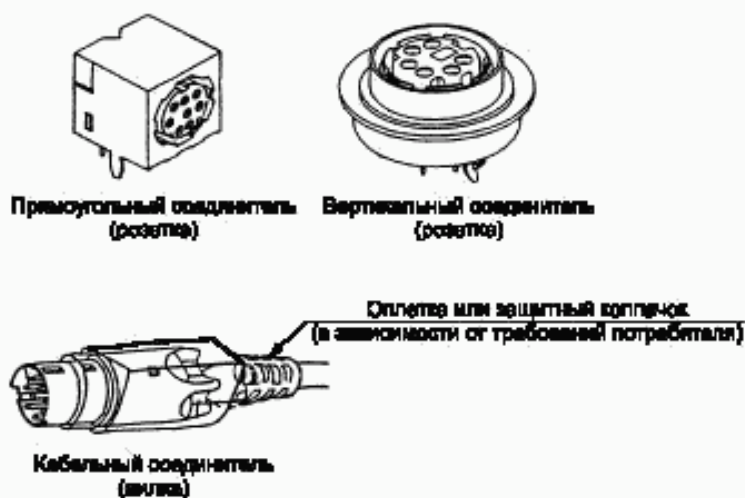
Общий вид соединителей в изометрической проекции
